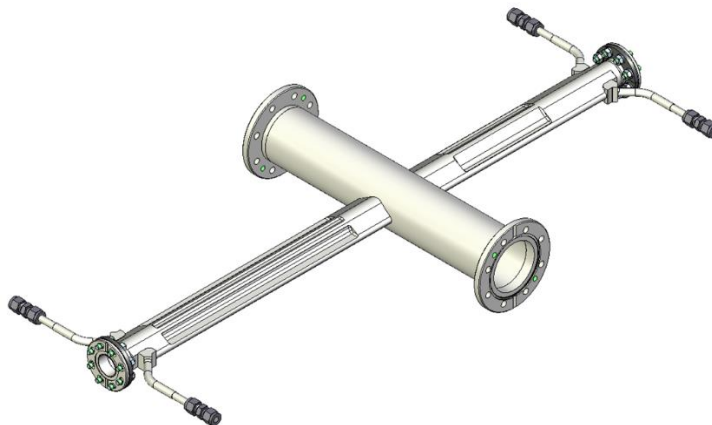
Внешний вид продольного сечения вакуумной камеры внутри патрубка откачного порта
